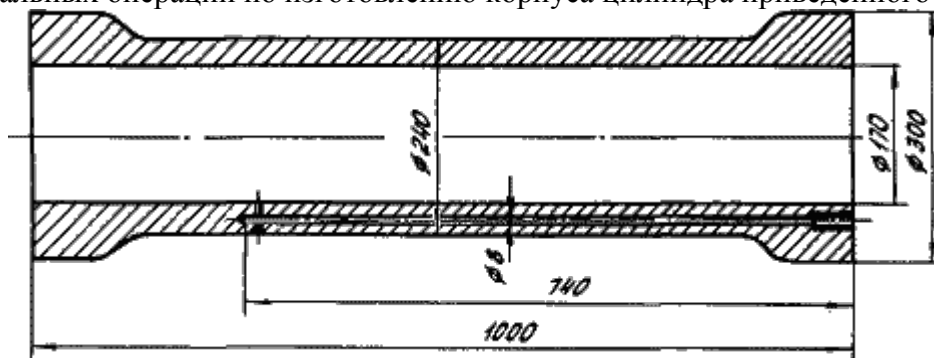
Пример нетехнологичной конструкции корпуса гидравлического цилиндра
